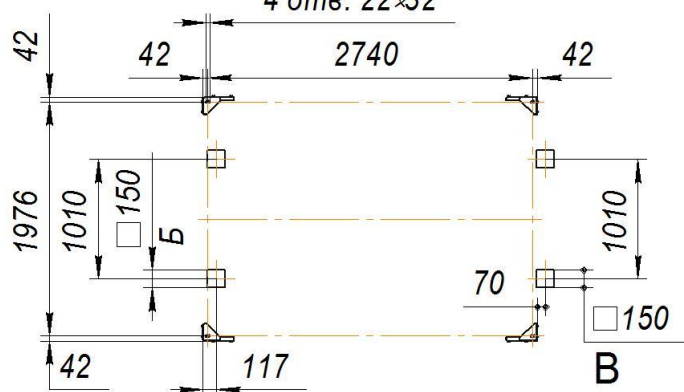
Установочные и присоединительные размеры блоков триеров БК-800-16 и БО-800-16:
